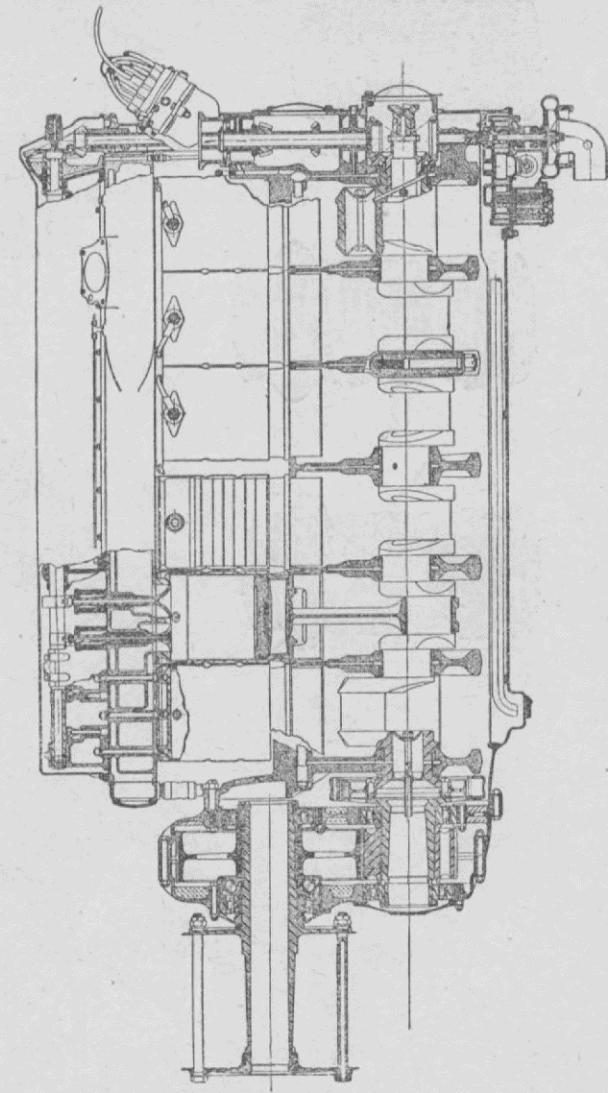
Поперечный разрез мотора Паккард 2A-1500, перевернутого типа.
